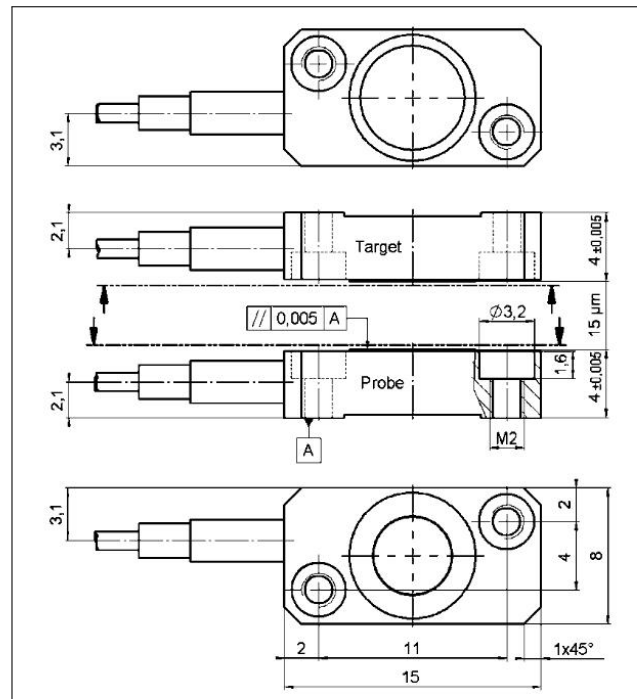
Dimensions du capteur D-015 (mm)
